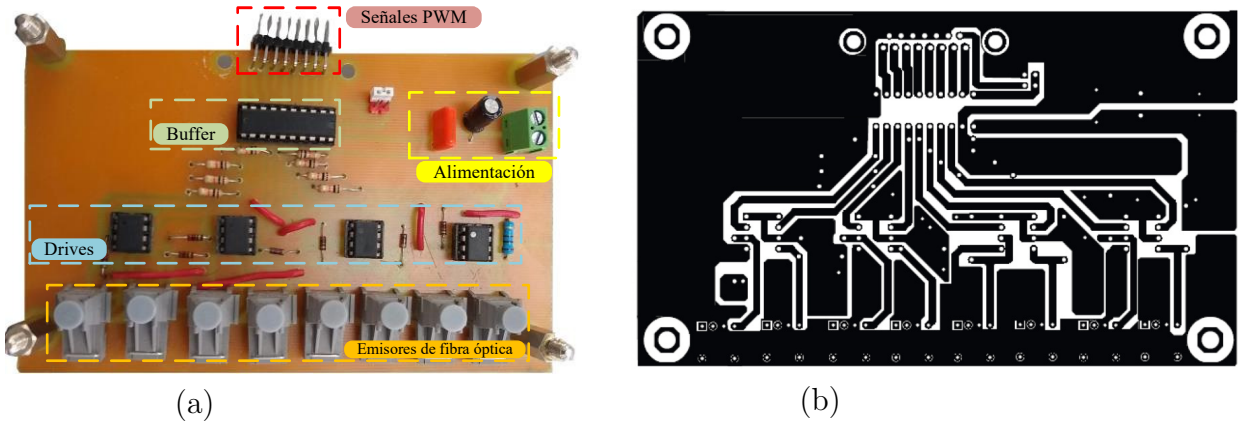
(a) Tarjeta de control implementada. (b) PCB de la tarjeta de control.
